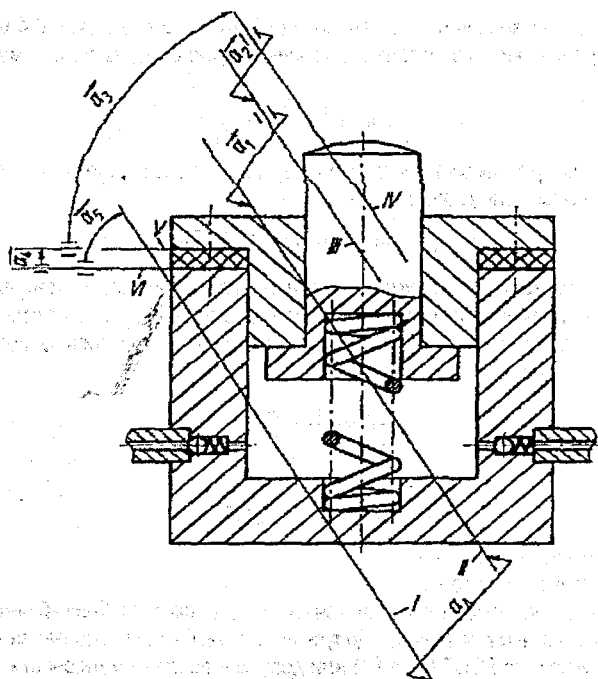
Схема угловой сборочной конструкторской размерной цепи для исходного звена от плунжерного насоса:
